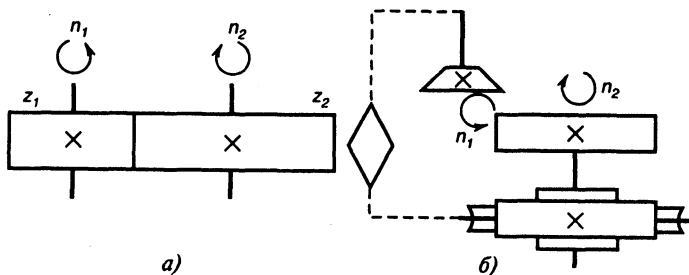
Обкат двух зубчатых колес (а), инструмента и заготовки (б)
